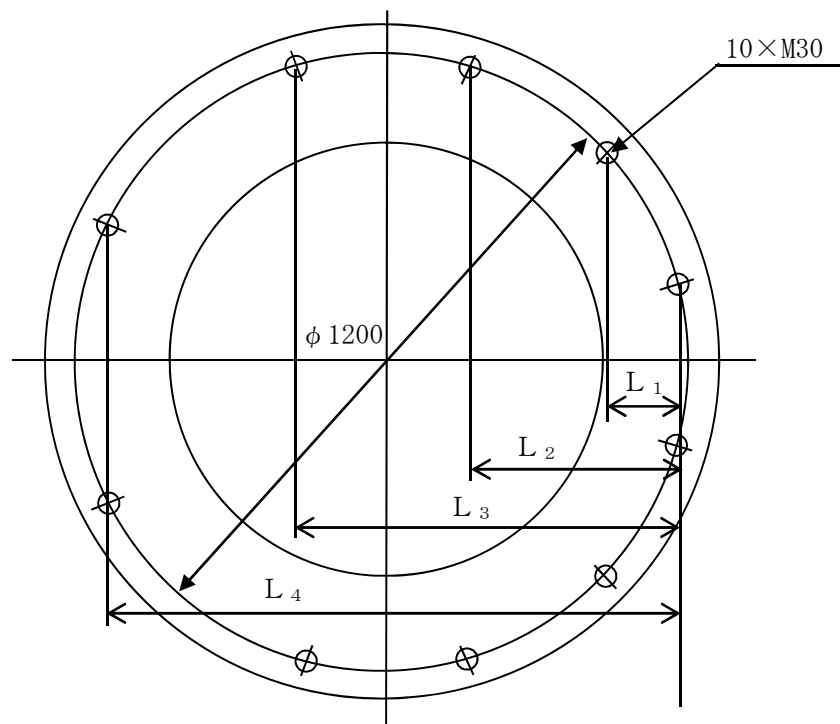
原動機台取付ボルトの各ボルト間寸法の配置図
